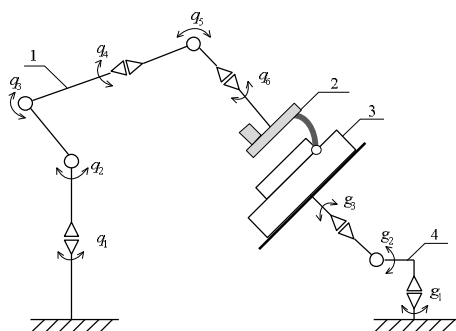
Схема роботизированного технологического комплекса для дуговой сварки
